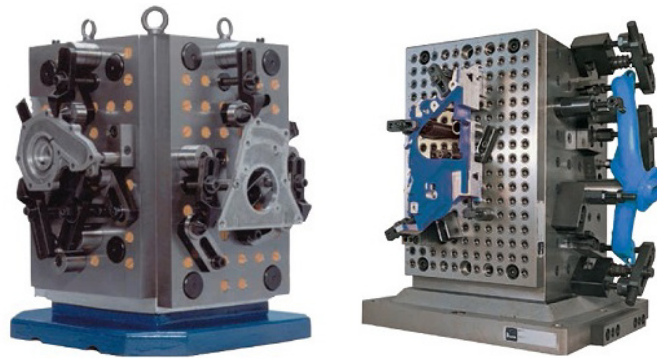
Модульні верстатні пристосування для установлення та закріплення корпусних деталей
